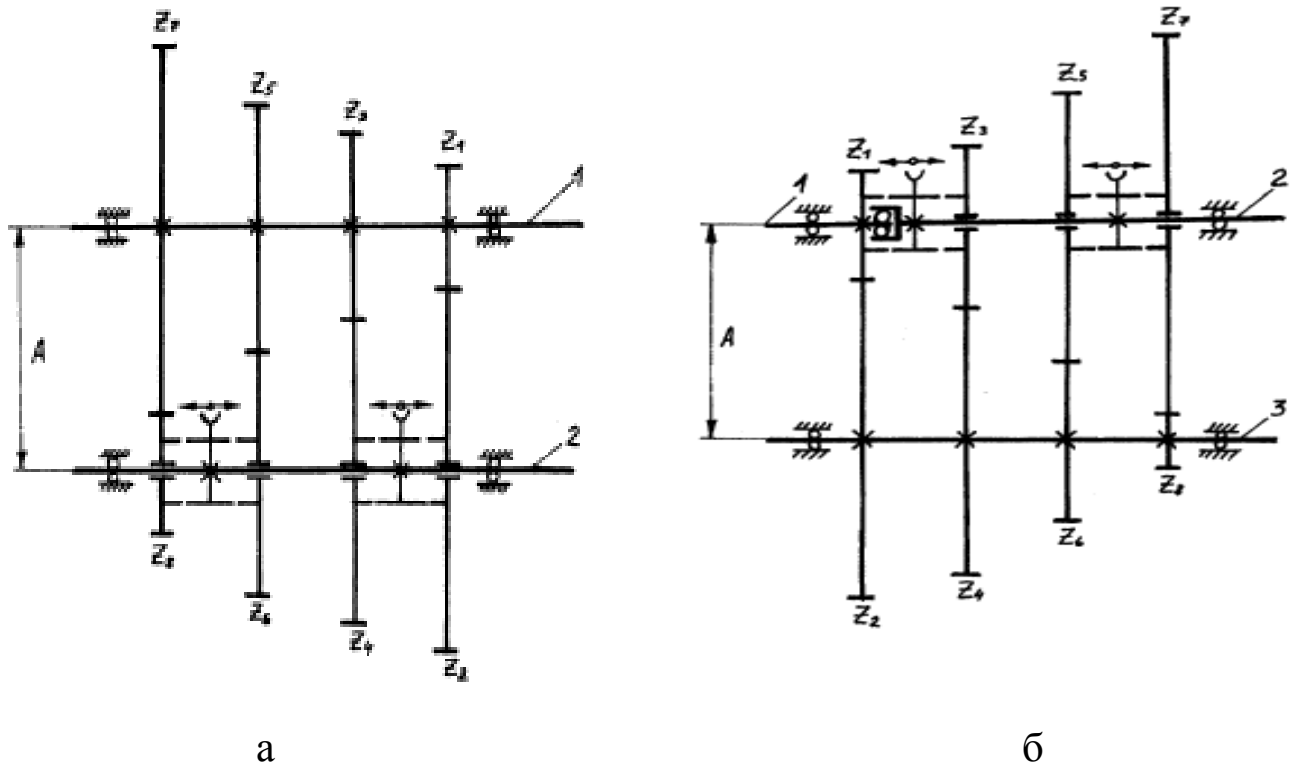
Принципиальная кинематическая схема четырехступенчатой коробки передач: а – двухвальной коробки передач, б – трехвальной коробки передач: 1 – ведущий вал; 2 – ведомый вал; 3 – промежуточный вал
